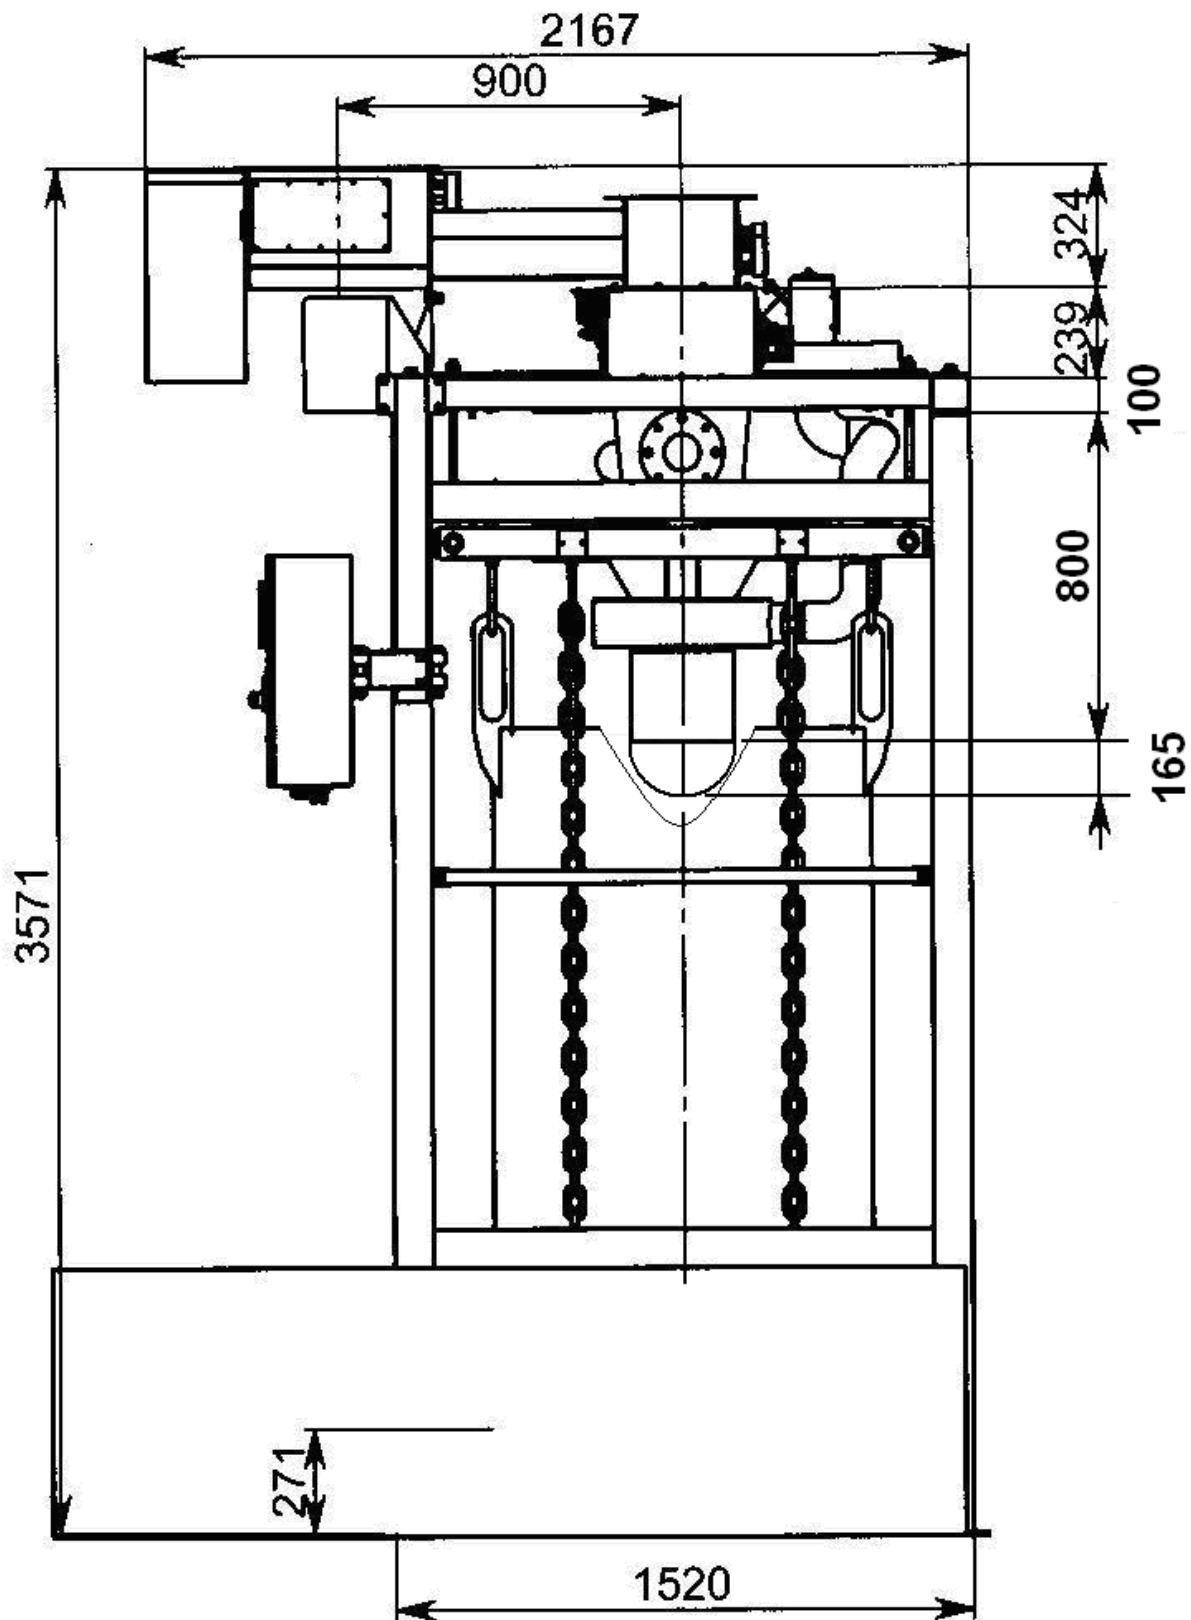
Габаритно-установочные размеры дозатора. Вид сбоку.
